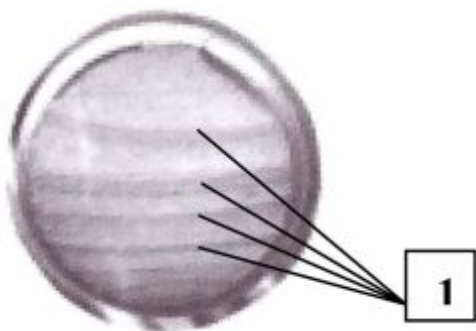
Усталостный излом шпильки крепления втулки воздушного винта: 1 - усталостные линии
